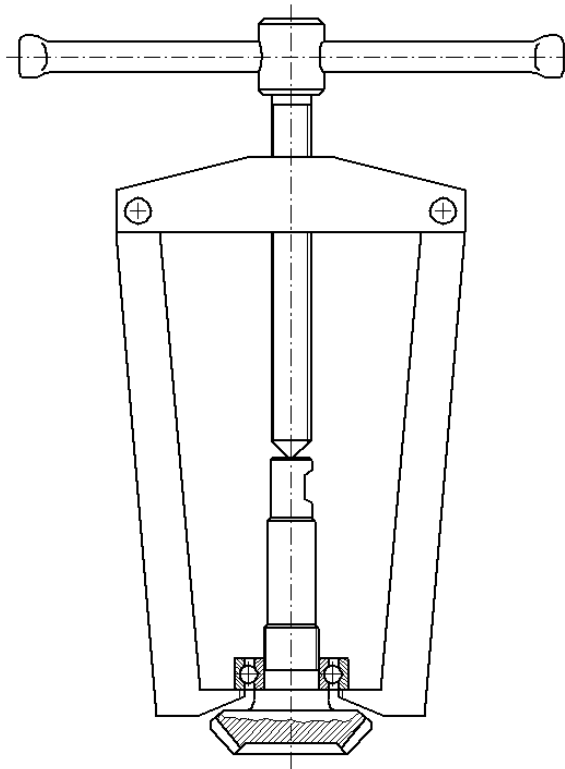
Проводиться вилучення підшипника із шестерні ведучої редуктора кутового.
